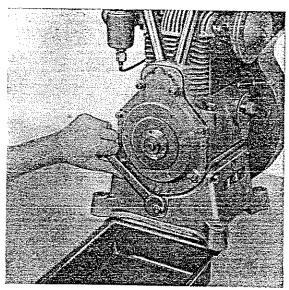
Desserrage de la vis sur la face arrière pour la vidange d'huile
